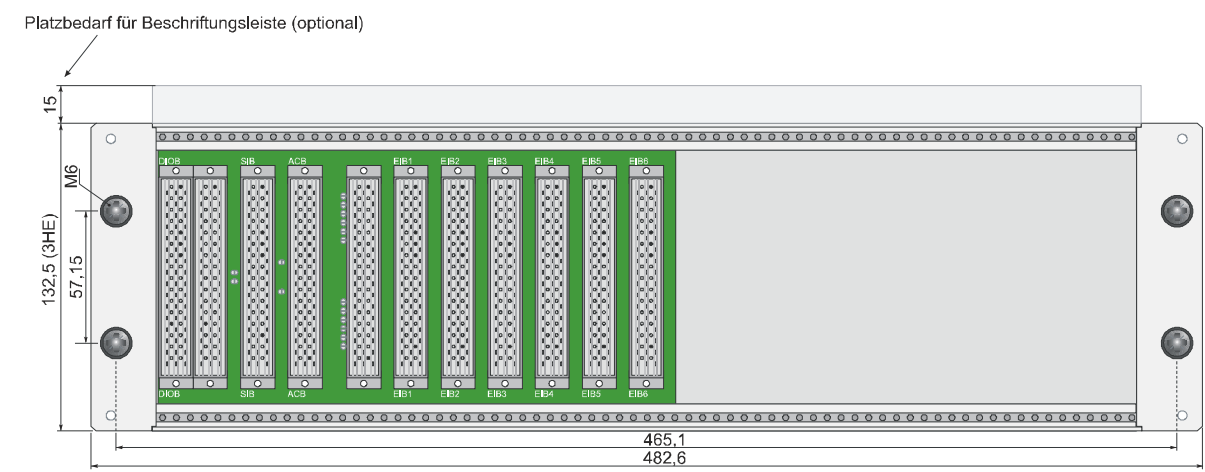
Vorderansicht des Baugruppenträgers Type BGT04 mit Beschriftungsleiste und einer ABP
